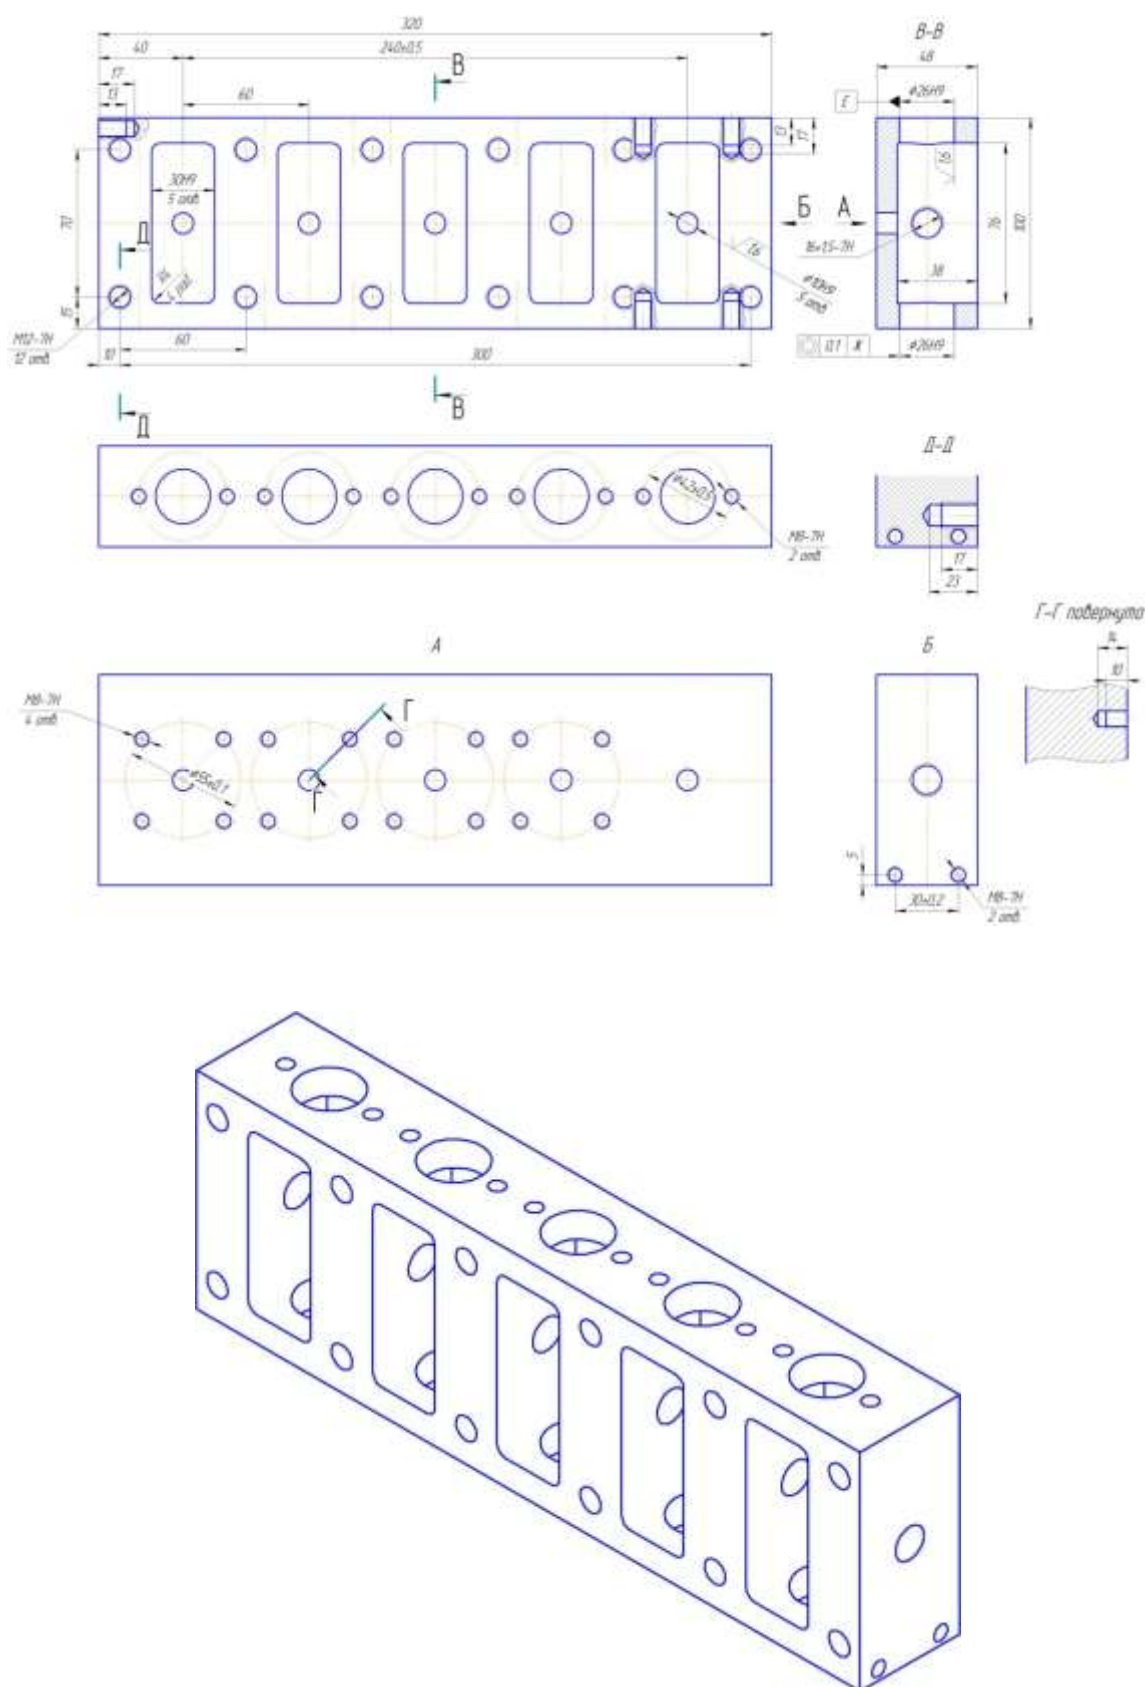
Кресленик та 3Д модель деталі «корпус»
